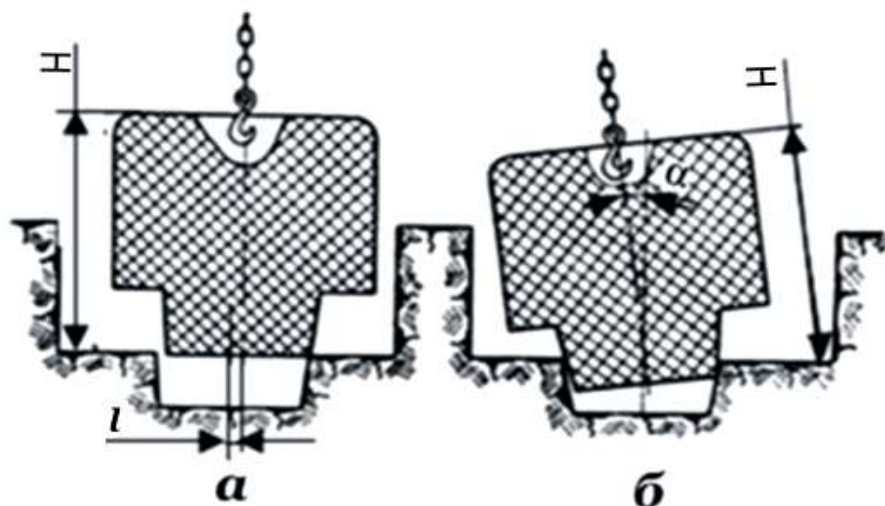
Схема возможного смещения кранового стержня при установке его в форму: а – горизонтальное смещение (линейное); б – угловое смещение
